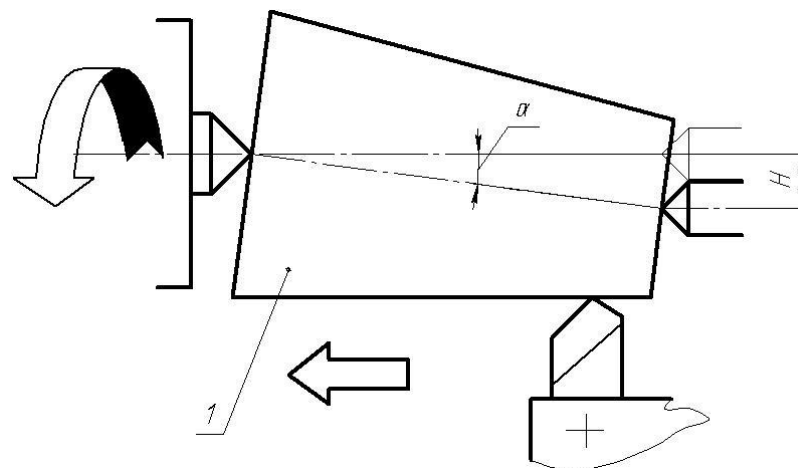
Обробка зовнішніх конічних поверхонь способом зміщення задньої бабки: 1 – заготовка
